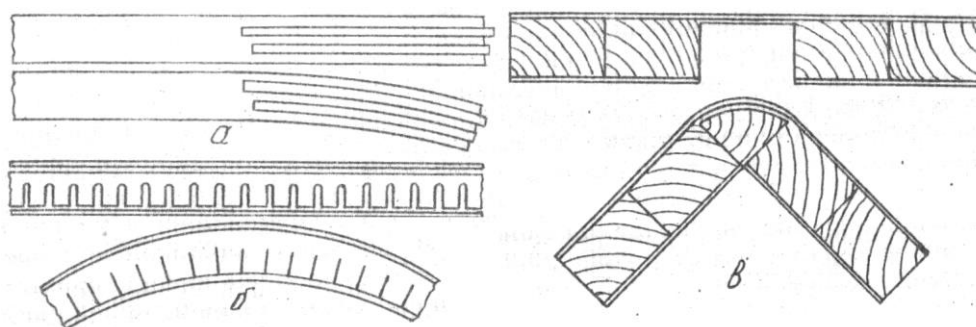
Способи формування криволінійних щитів: а - з поздовжніми пропилами на кінцях заготовки; б — з поперечними пропилами на пласті заготовки; в - з пазом і бобишкою
